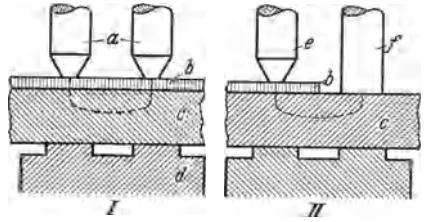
Grundform der Doppelpunktschweißung.
